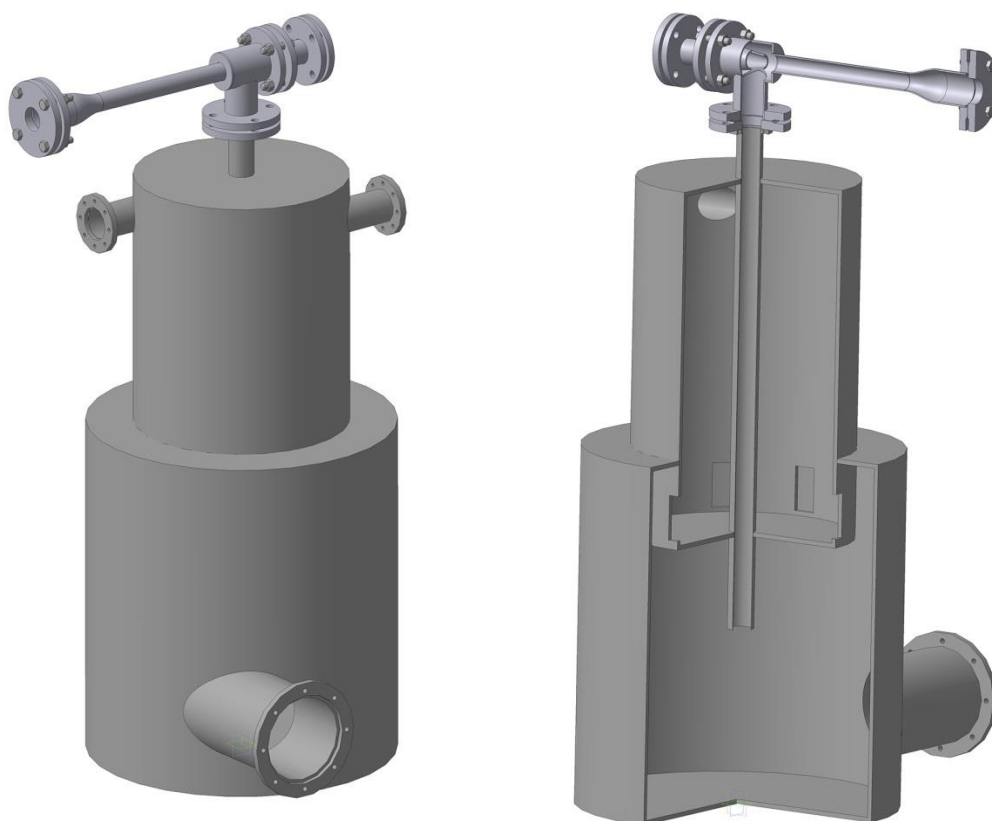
Общий вид центробежно-вихревого сепаратора
